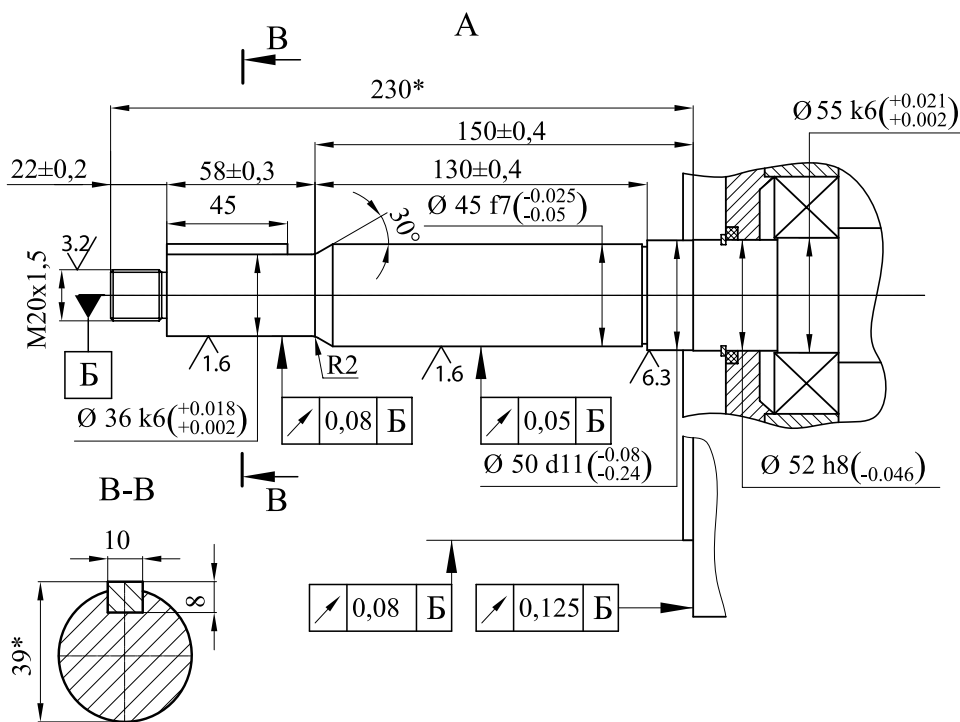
Свободный конец вала двигателя 6АМУ160М4ЖУ2
